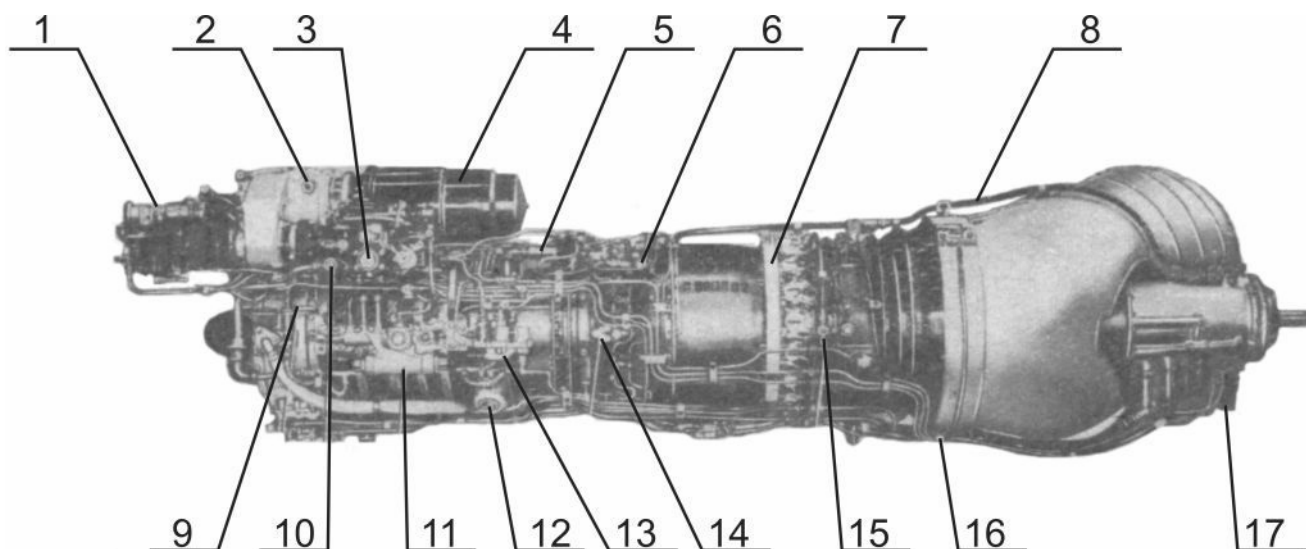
Двигатель ТВ2-117А (вид слева):
